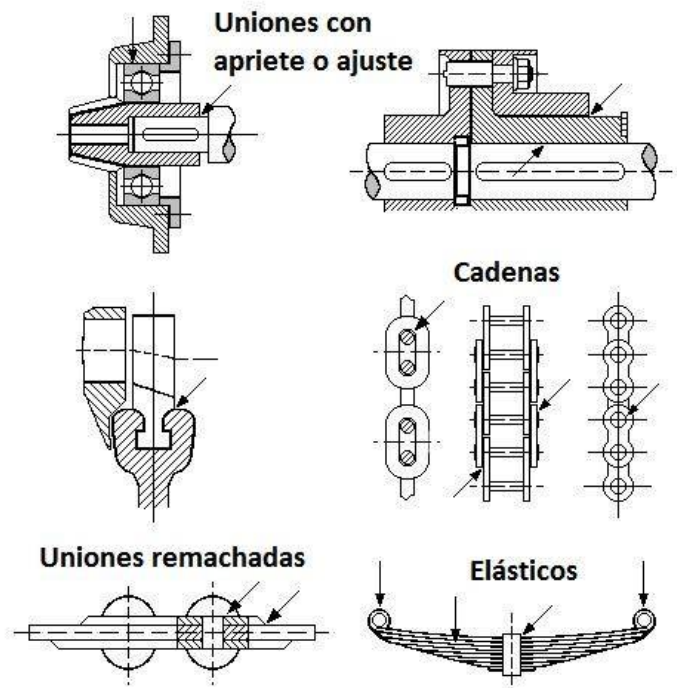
Tribo-corrosión en elementos mecánicos que poseen montaje con ajuste.
